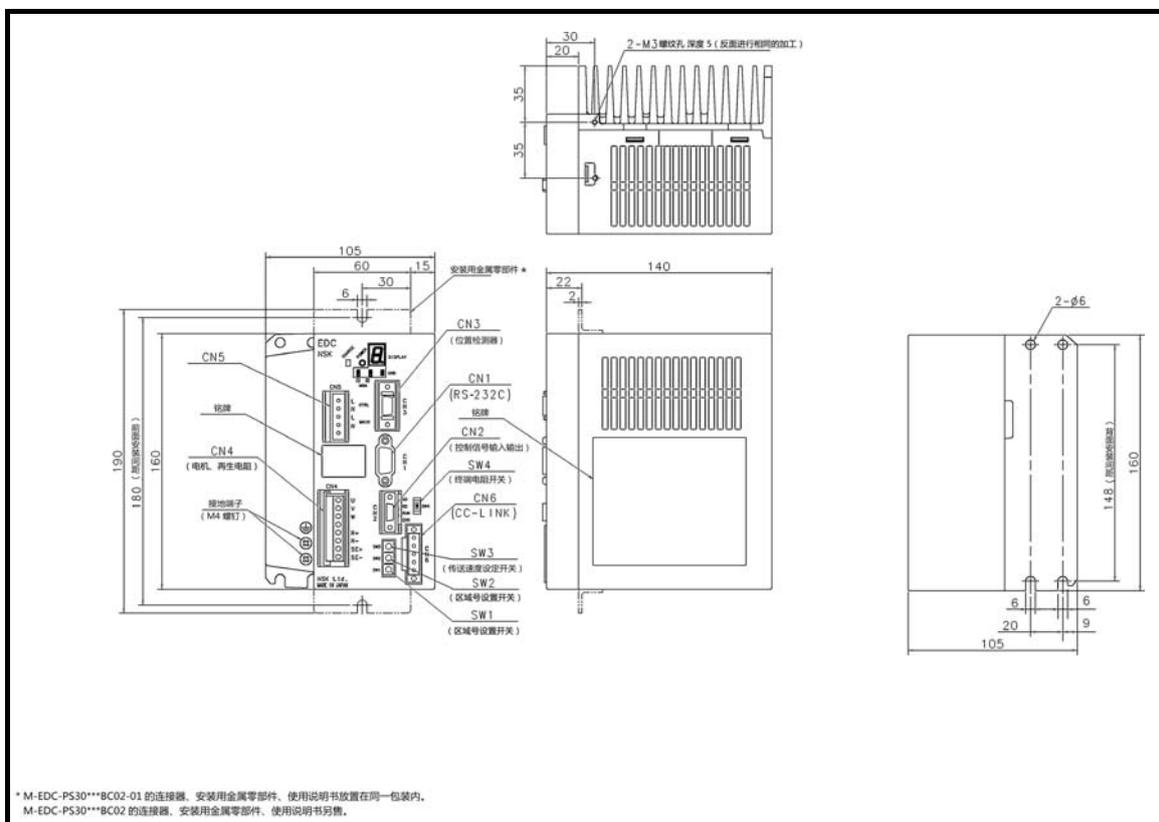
支持 CC-Link 的 EDC 型驱动器外形尺寸
